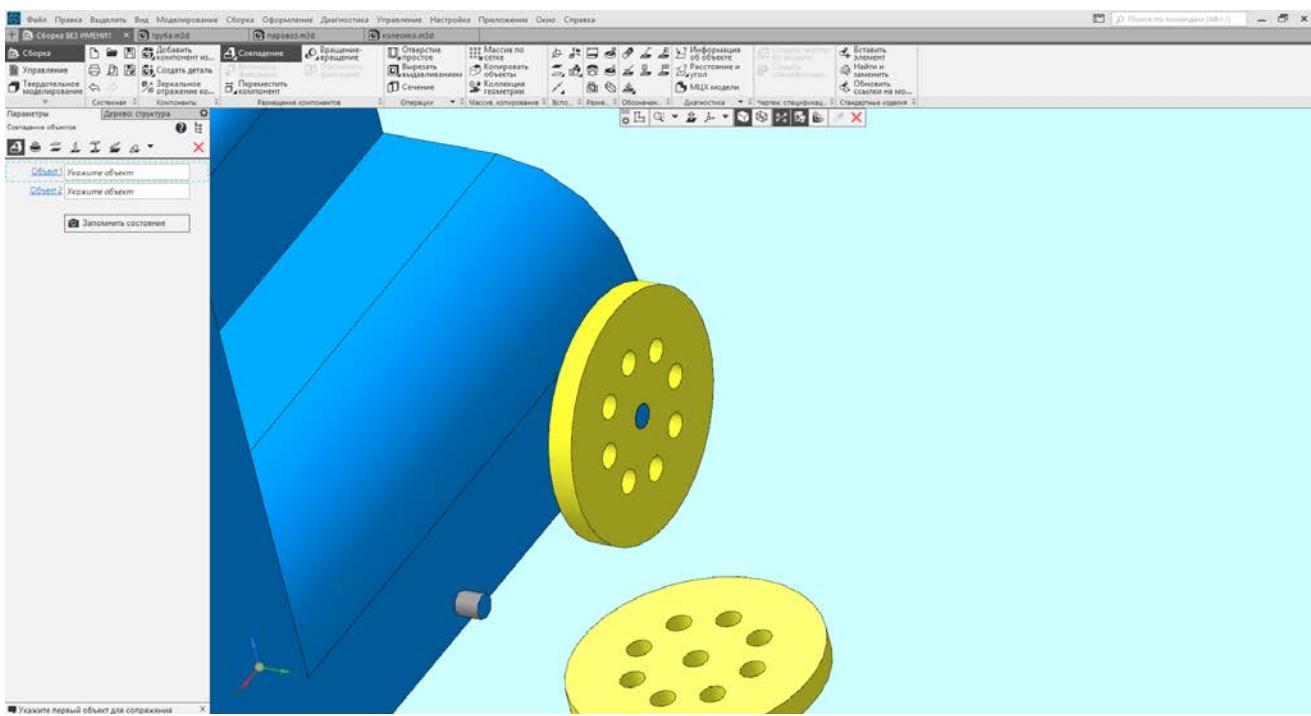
Применение команды «Совпадение» для передней поверхности колеса и крепления под колеса на корпусе паровоза
